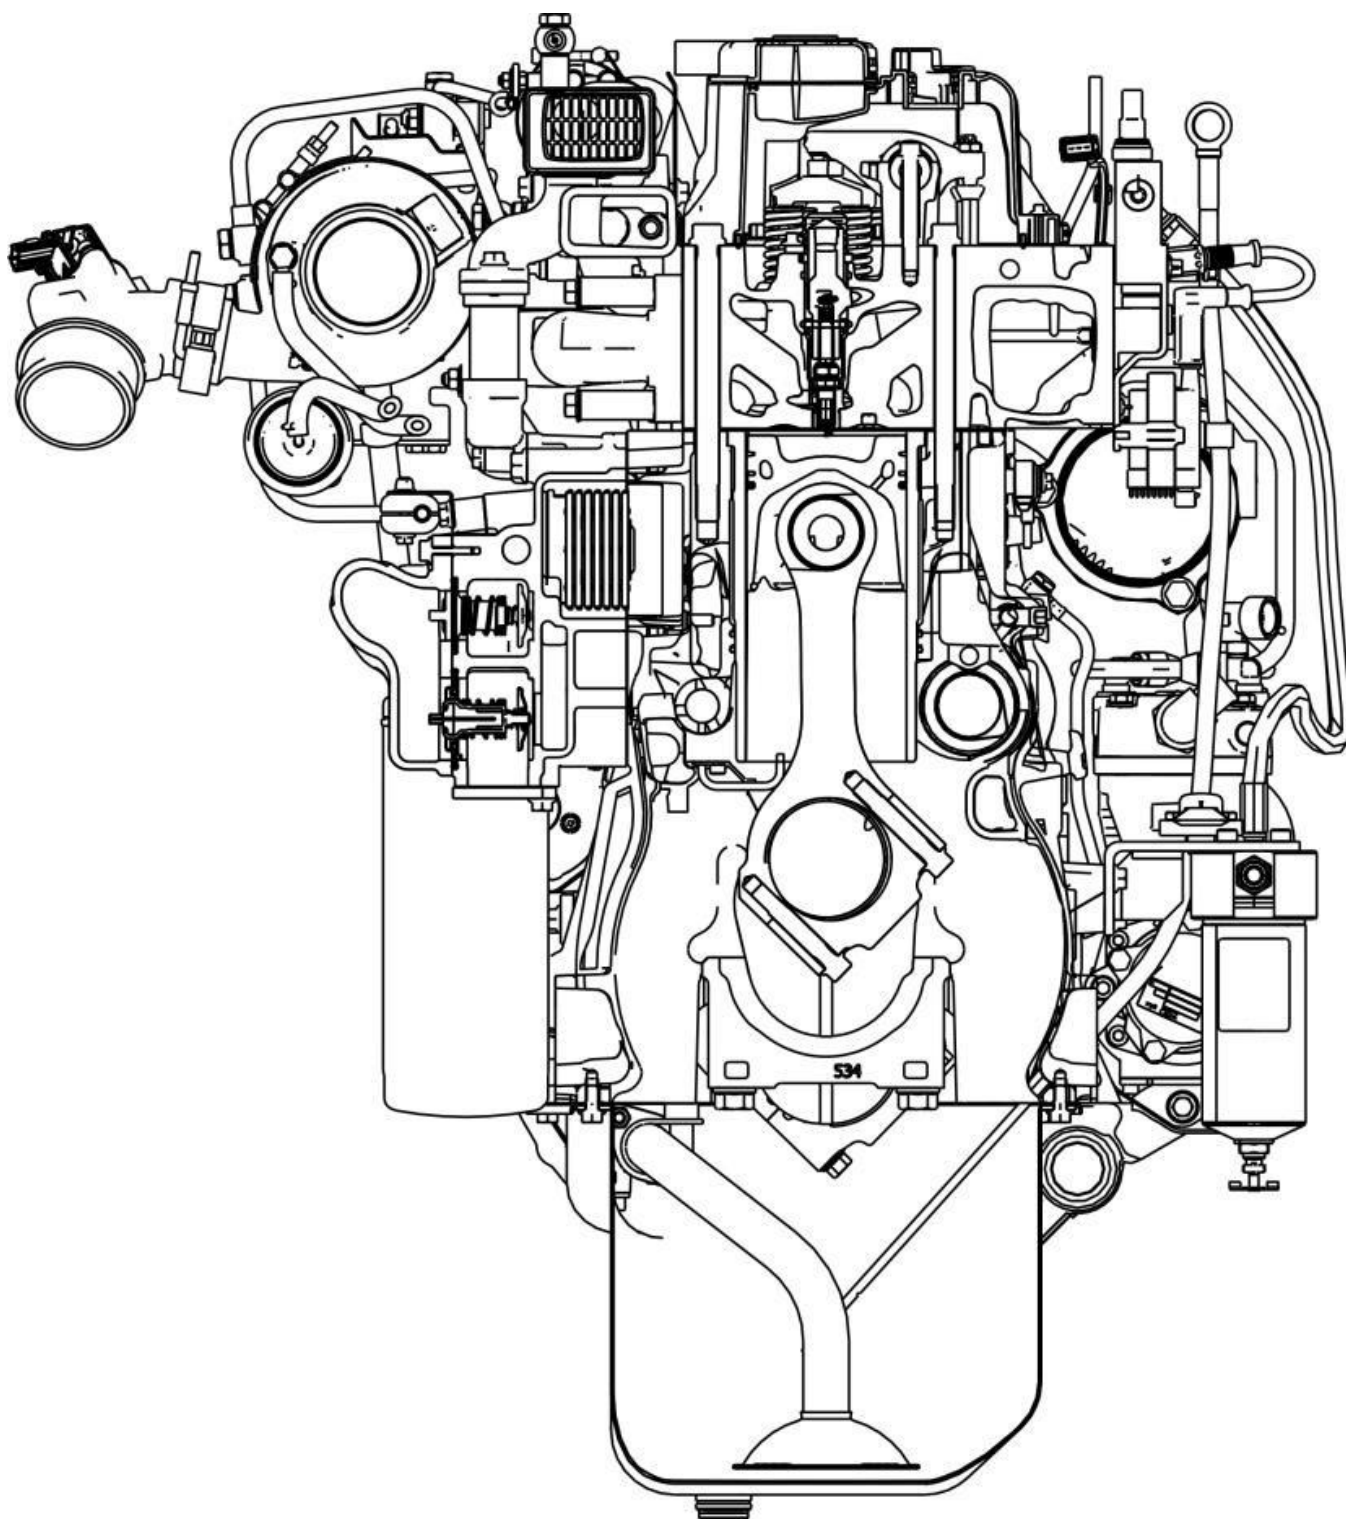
Поперечный разрез двигателя ЯМЗ-53444-20
